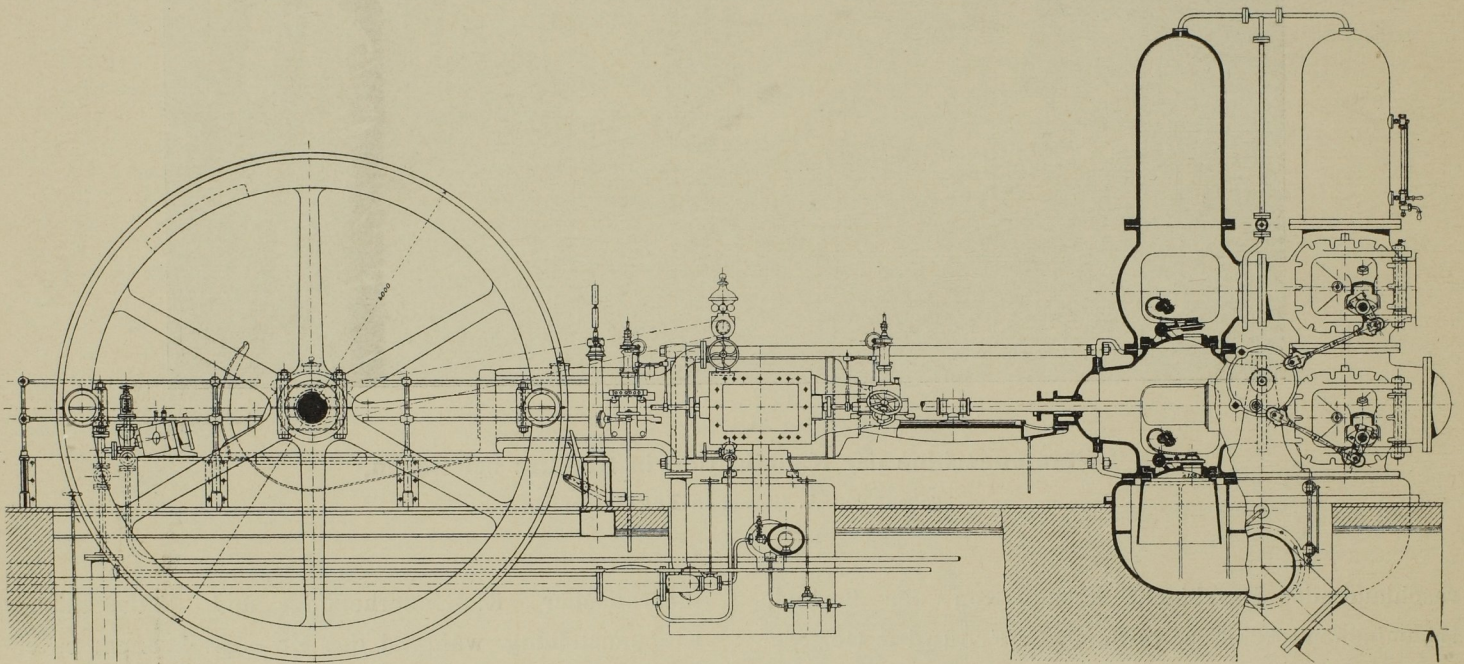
Seitenansicht und Schnitt der Pumpmaschine.
